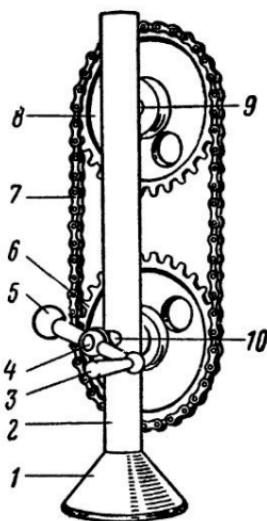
Модель цепной передачи: 1 — основание; 2 — стойка; 3 — ручка; 4 — вал привода; 5 — рычаг ручки; 6 — ведущая звездочка; 7 — цепь; 8 — ведомая звездочка; 9 — ось ведомой звездочки; 10 — упорная втулка.
